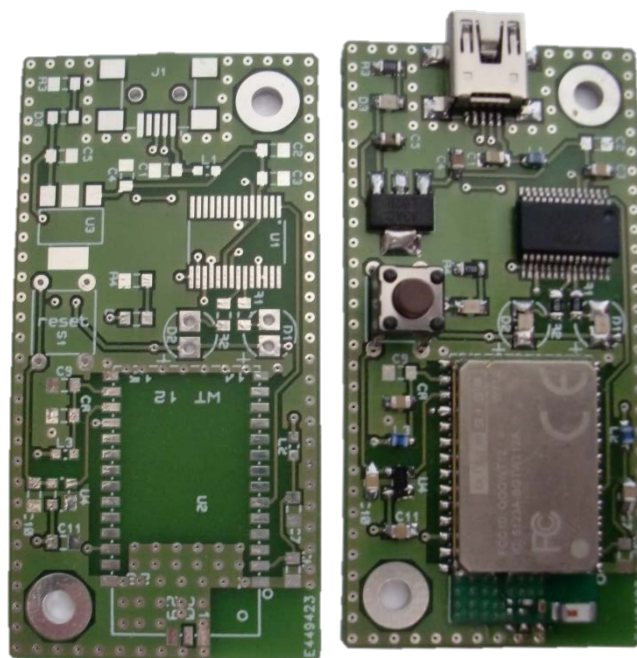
Aspecto final da PCB após produção (à esquerda) e após montagem (à direita).
